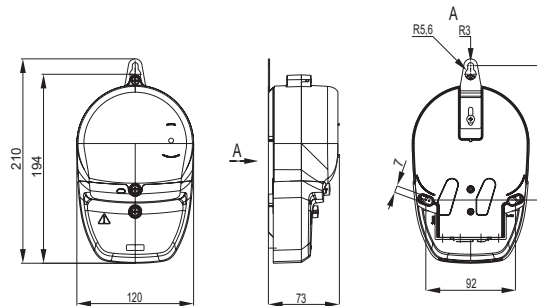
Габаритные и присоединительные размеры счетчиков габарита 2
